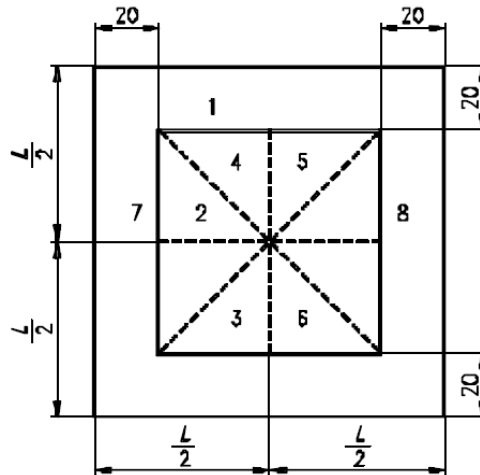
Esquema das posições para a medição do desvio da planeza
